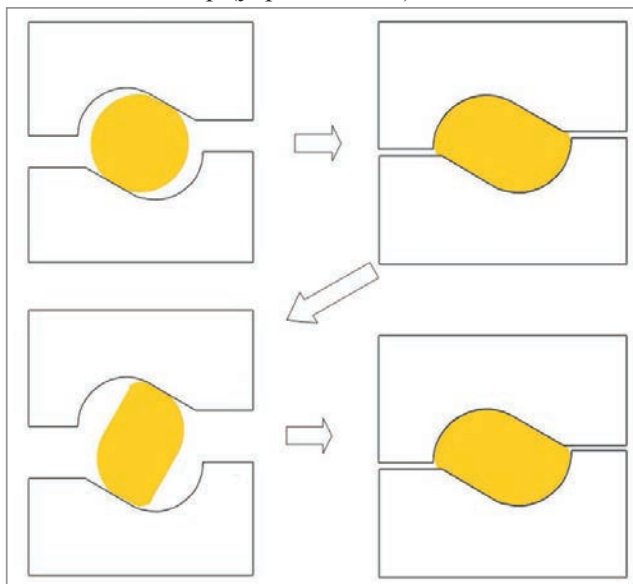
Схемаковки (протяжки) заготовок в бойках новой конструкции
